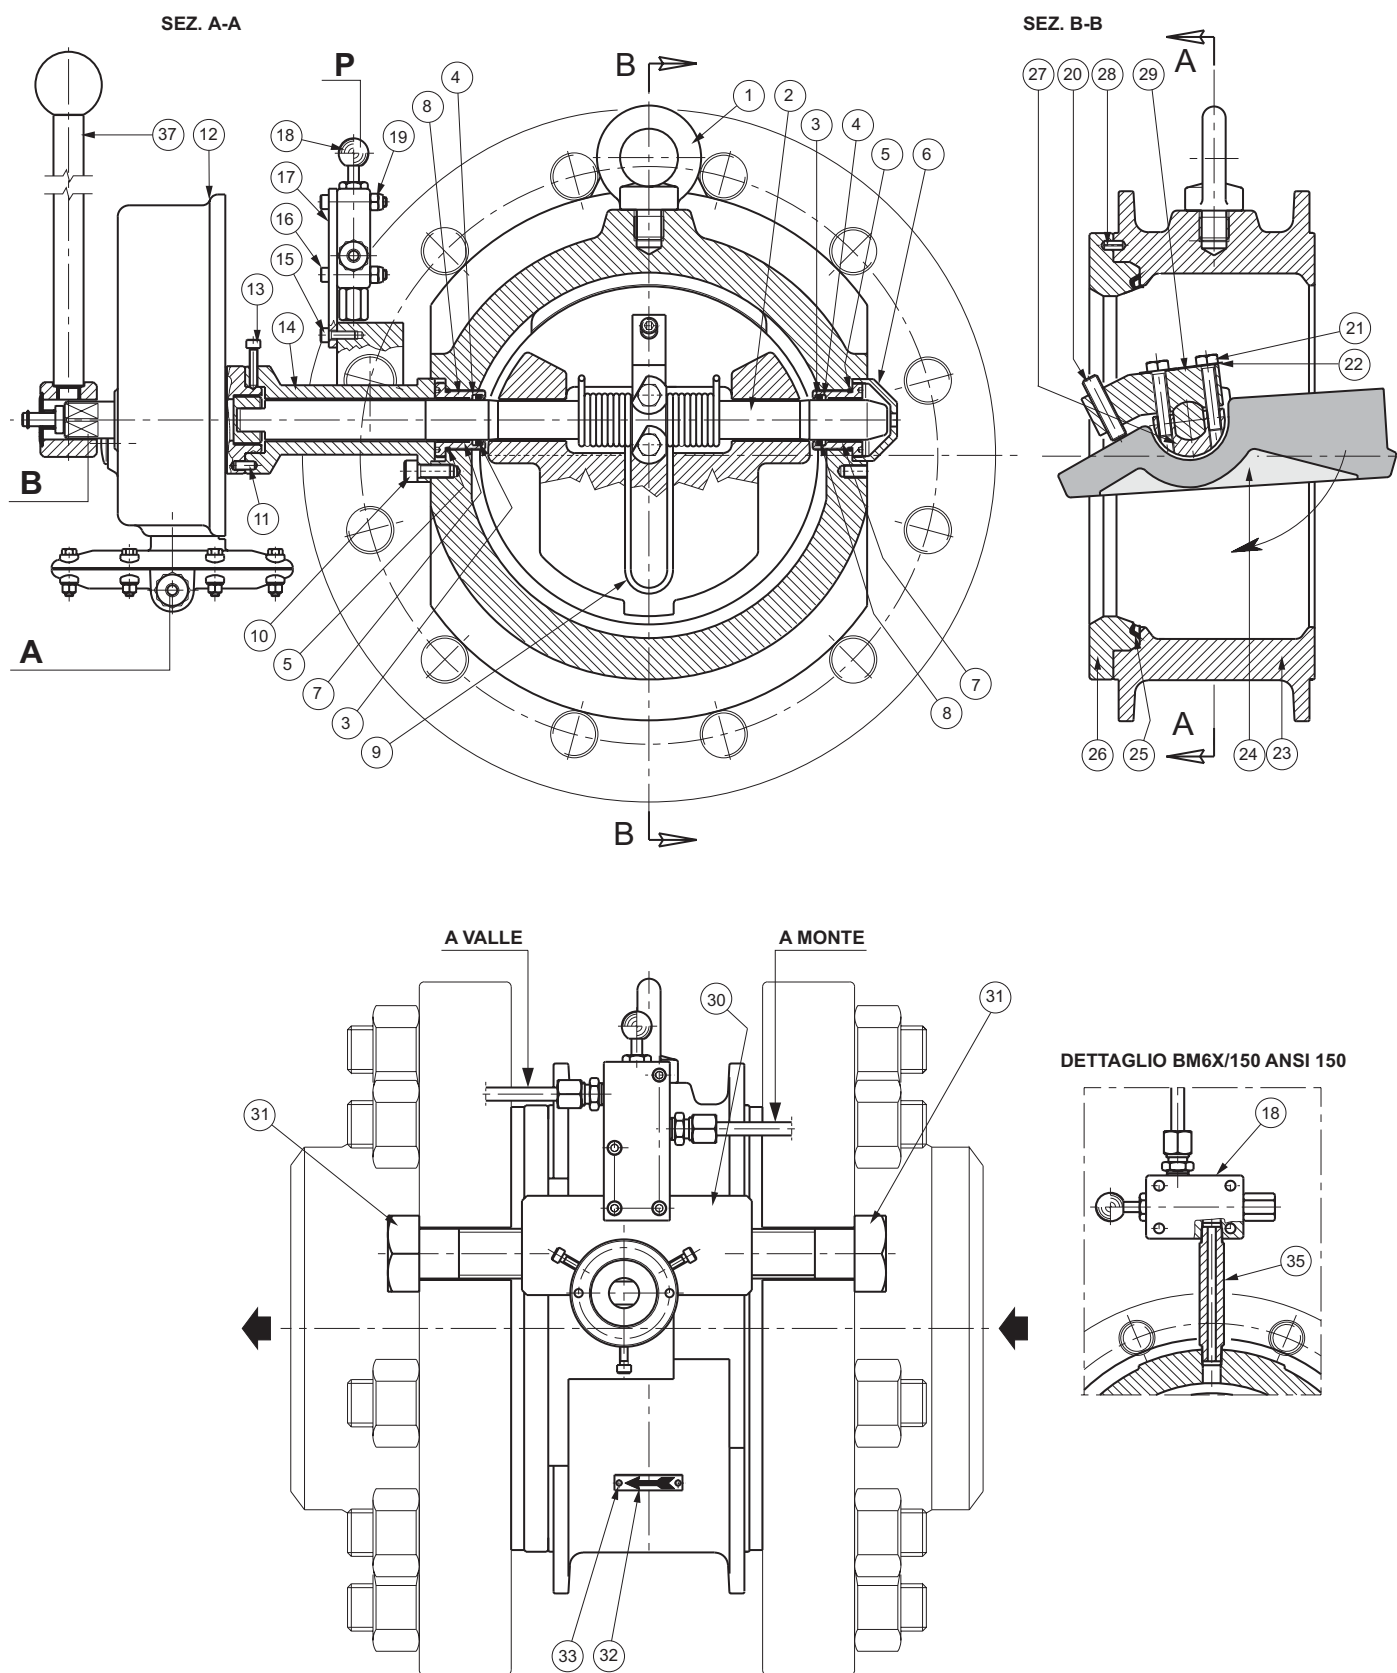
Valvola di Blocco Tipo BM6X DN 80/100 Versione Casting
